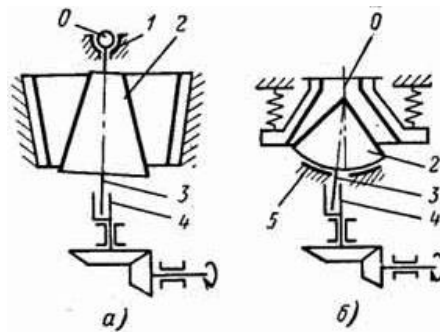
Кінематичні схеми конусних дробарок
